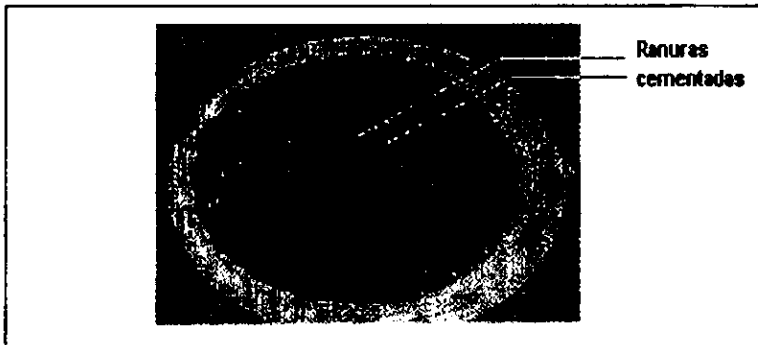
Sección limpia de tubería expandible ranurada en fibra cemento.
